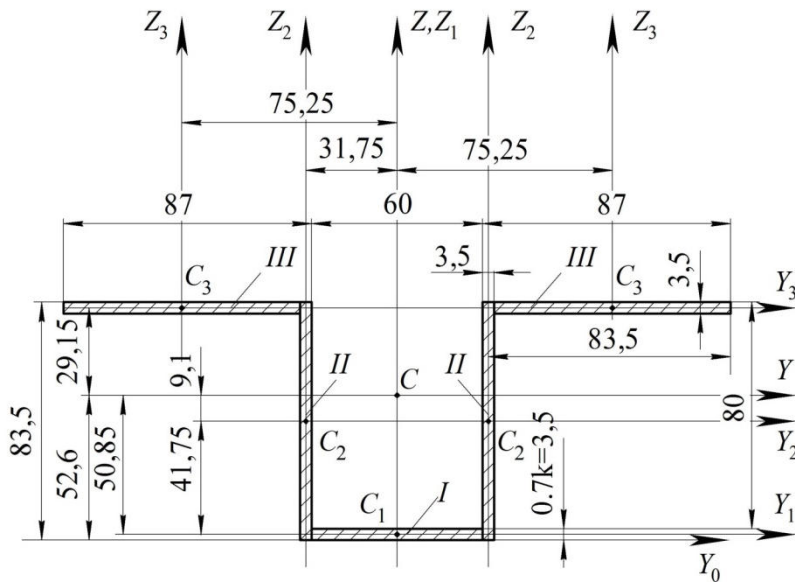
Зварне з'єднання поперечини із несучою балкою
